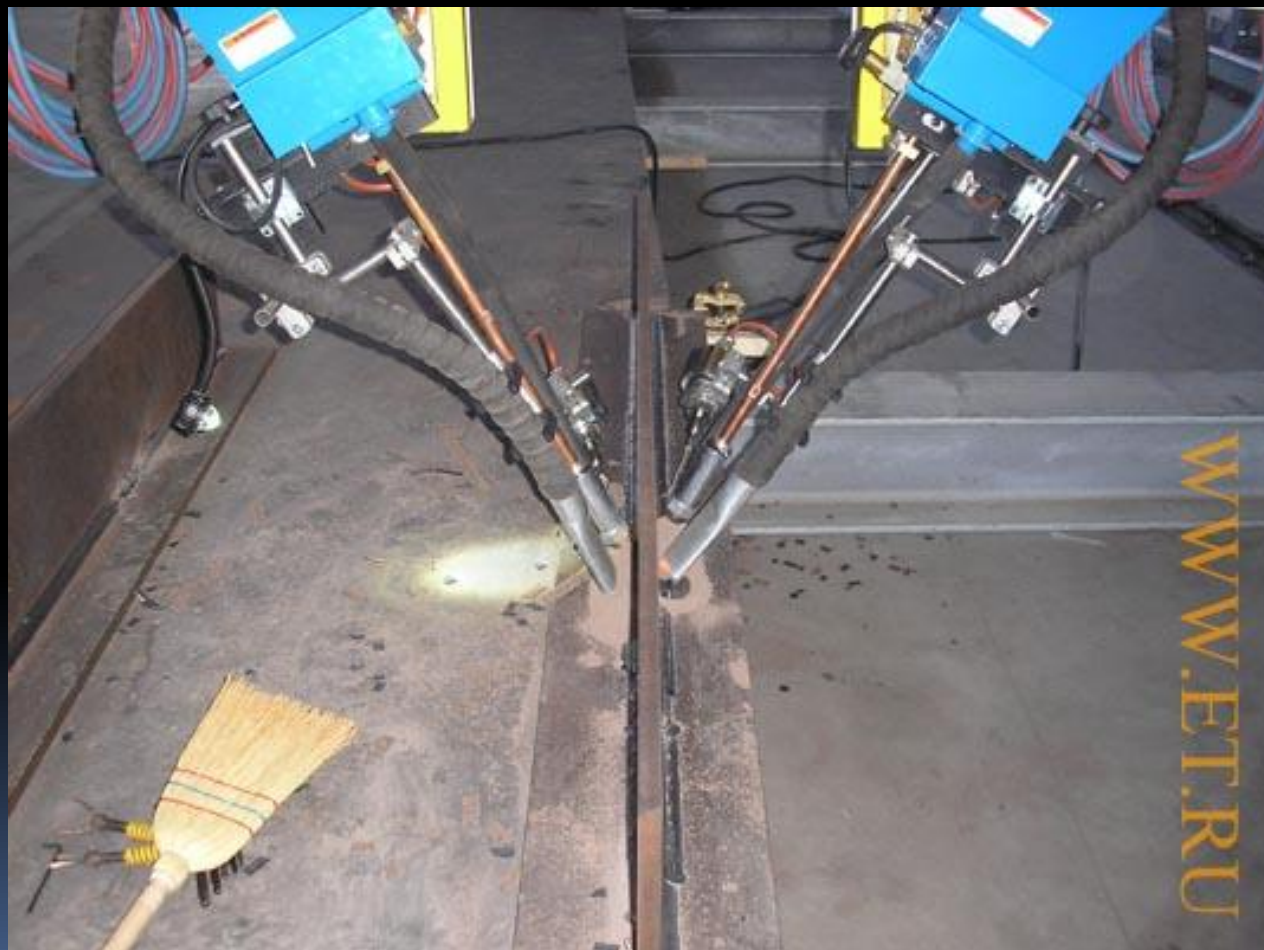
Установка для одновременной сварки двух швов балок:
